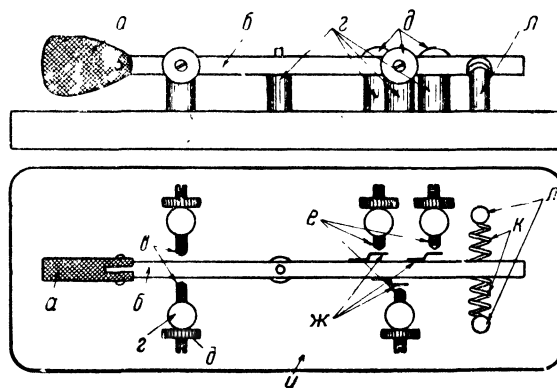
Устройство ключа манипулятора: а — ручка; б — корытцо; в — упорные винты; г — стойки; д — стопорные гайки; е — контактные винты; ж — пружинящие контакты; к — пружина; л — стойки для крепления пружины
